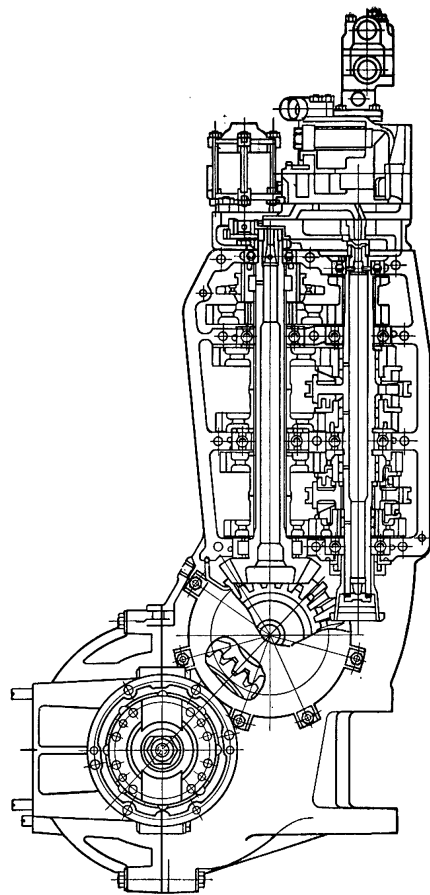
Моноблочная конструкция главной передачи и коробки передач
